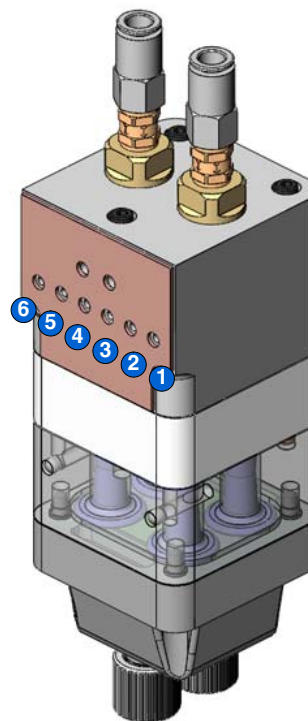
Magnetventils og luftreguleringsventils funktioner
